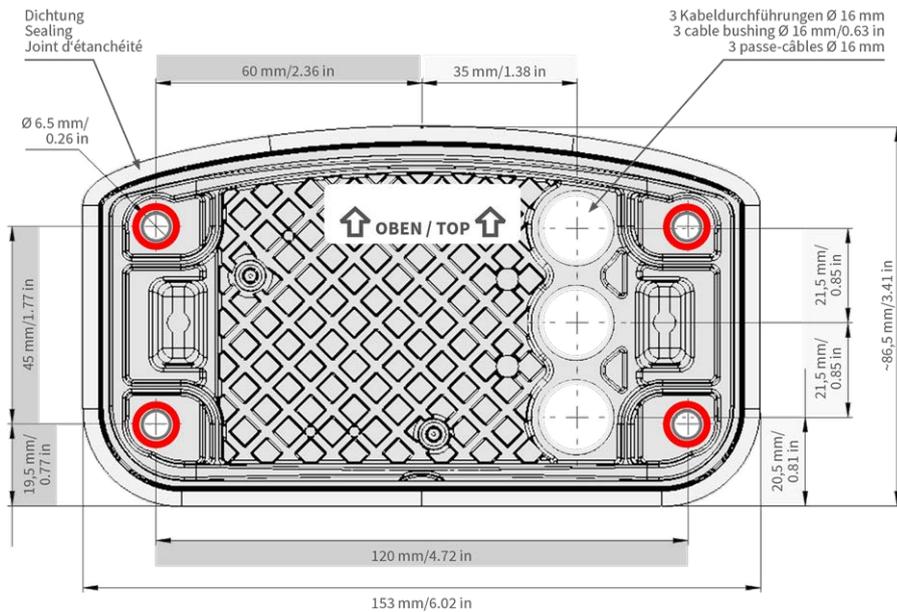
Montageplatte mit Bohrungen zur Positionierung der Befestigungsschrauben
